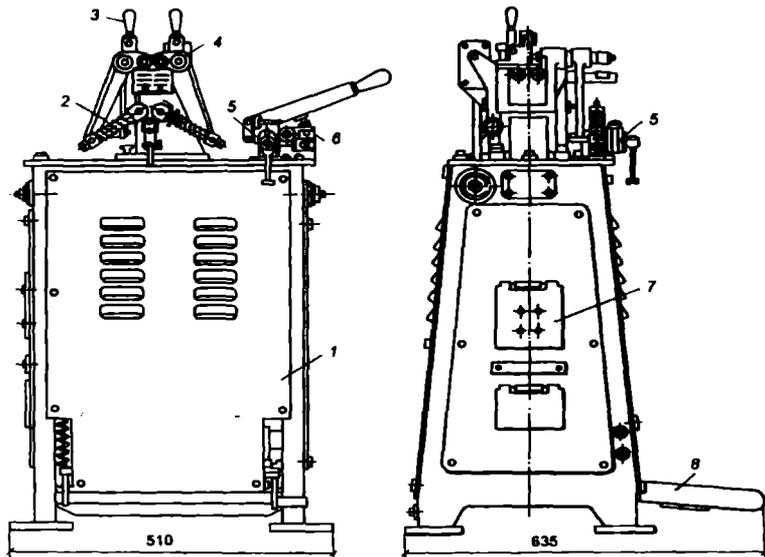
Машина МС-502 для стыковой сварки:
